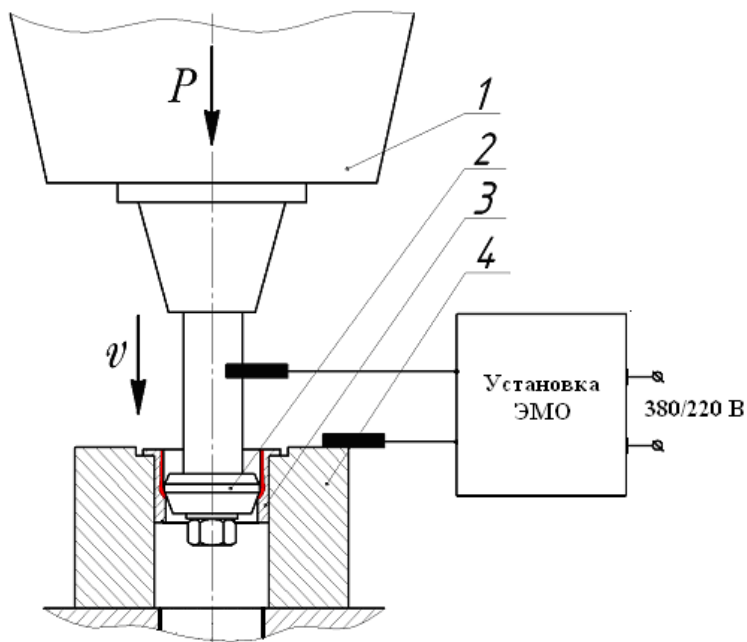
Схема процесса ОЭМД: 1 – вертикально-фрезерный станок; 2 – инструмент; 3 – втулка; 4 – обойма
